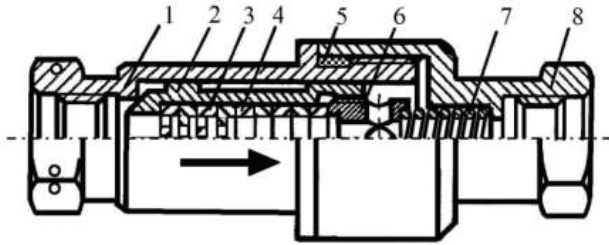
Односторонний дроссель, где 1- корпус; 2- клапан; 3- дроссельная шайба; 4- регулировочное кольцо; 5- уплотнительное кольцо; 6- упор; 7- пружина; 8- крышка
